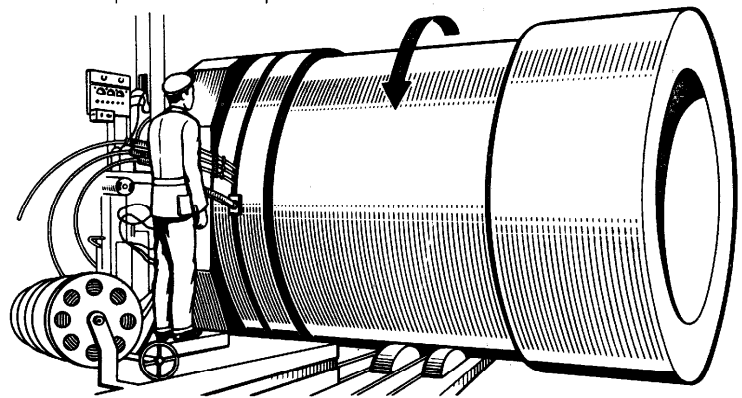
Электрошлаковая сварка кольцевого шва цилиндра прессы
